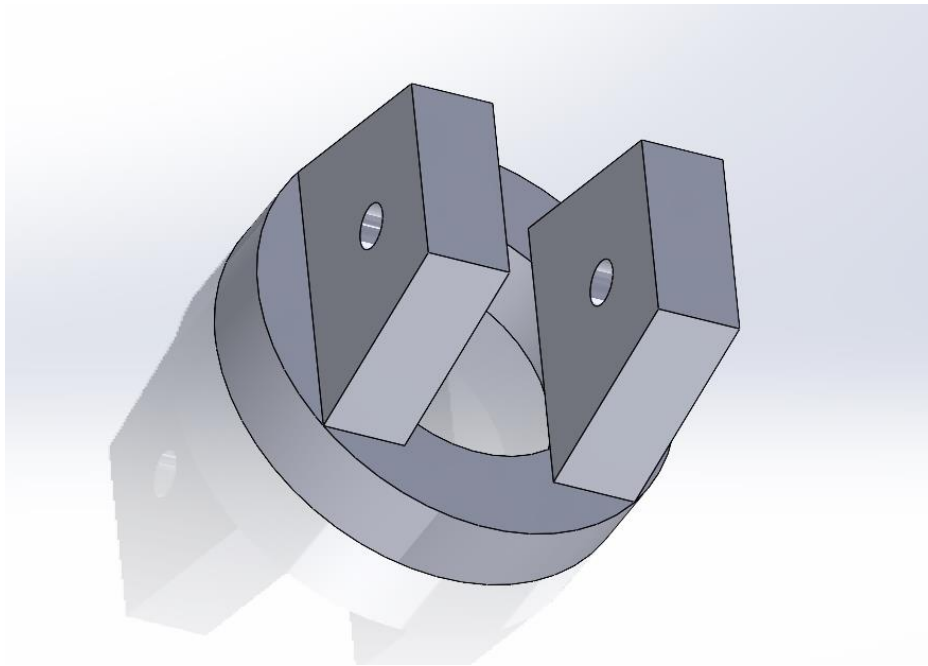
14. Khớp thanh truyền – hình ảnh 3D
